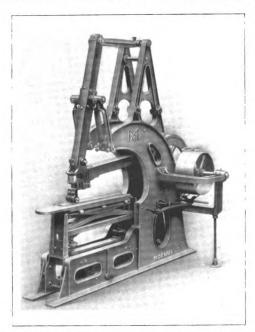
Glanzstoß-Maschine mit horizontaler Stoßbahn und federndem Werkzeugkopf.
